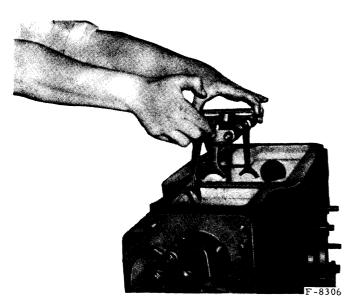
Dégagement de l'ensemble coulisseauxfourchettes.
